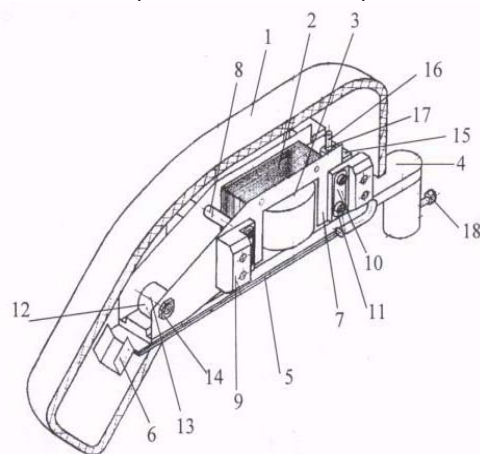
Конструкция электромагнитного вибратора: 1 – корпус; 2 – сердечник; 3 – катушка; 4 – электрододержатель; 5 – якорь электрододержателя; 6 – клемма; 7 – кармашковая пластина; 8 – втулка, демпфер; 10 – пластина; 11 – винт М3; 12 – втулка; 13 – ось; 14 – гайка М6; 15 – корпус регулятора зазора; 16 – ось регулятора; 17 – гайка М5; 18 – винт прижимной
